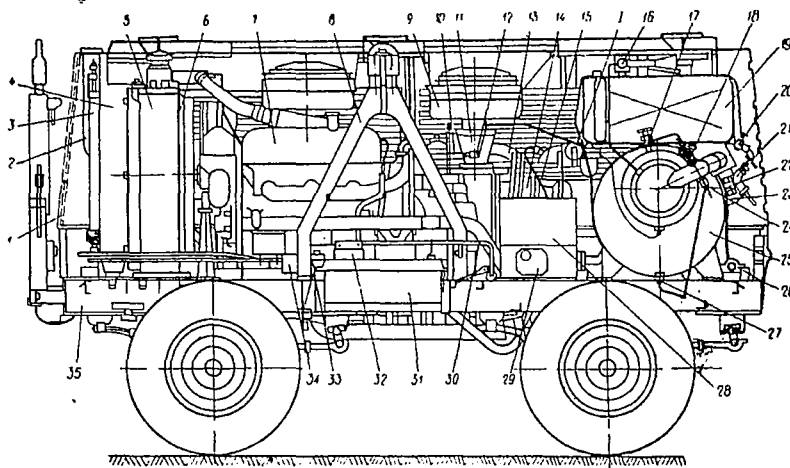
Передвижная компрессорная станция ПВ-10 (конструктивная компоновка)
